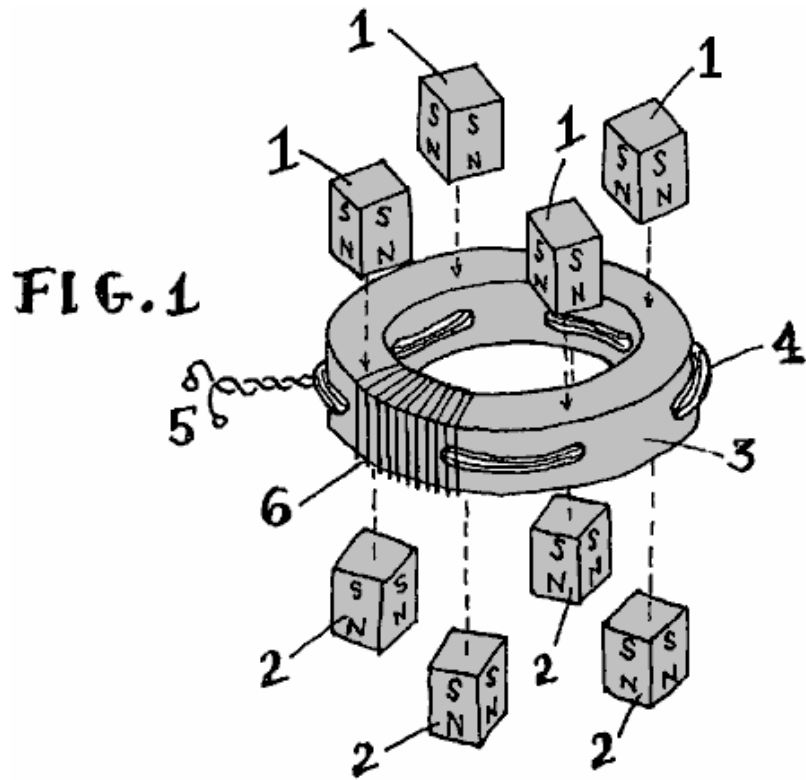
ist eine Explosionsansicht des Generators dieser Erfindung.
